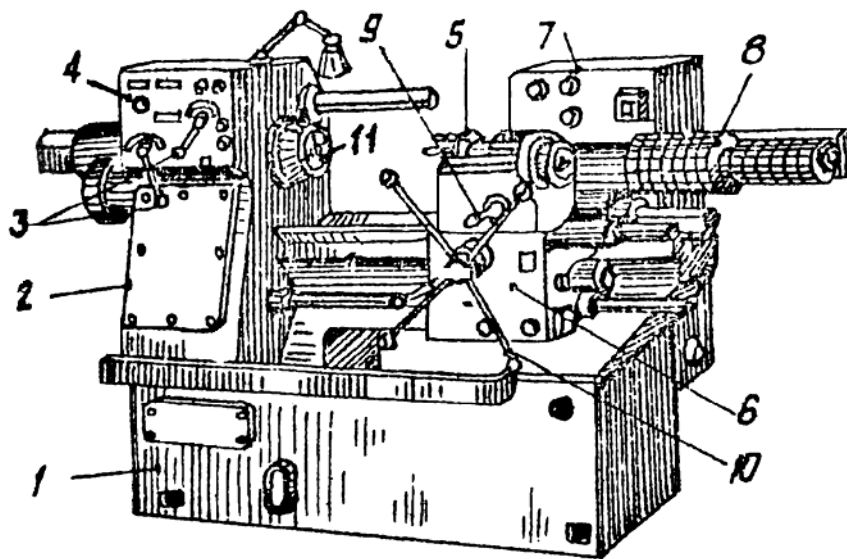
Загальний вигляд токарно-револьверного верстата:
